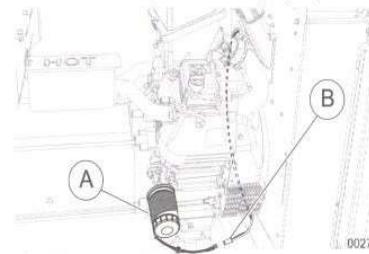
Установка обогревателя масляного фильтра (11–22 кВт)
